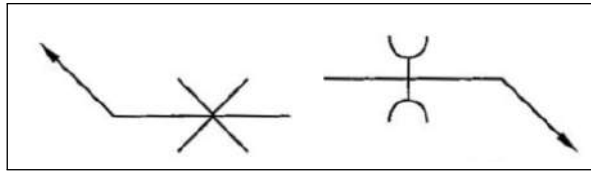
Aplicación de Símbolos de soldaduras simétricas
